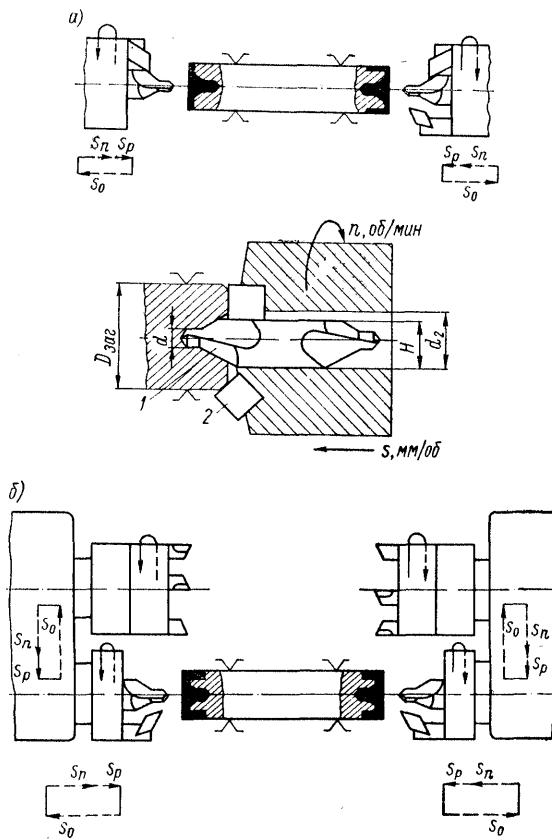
Схема обработки торцов заготовок инструмента диаметром 10—50 мм и комбинированный блок инструментов, используемый при работе по этой схеме (а), схема обработки торцов заготовок инструмента диаметром выше 50 мм (б)
